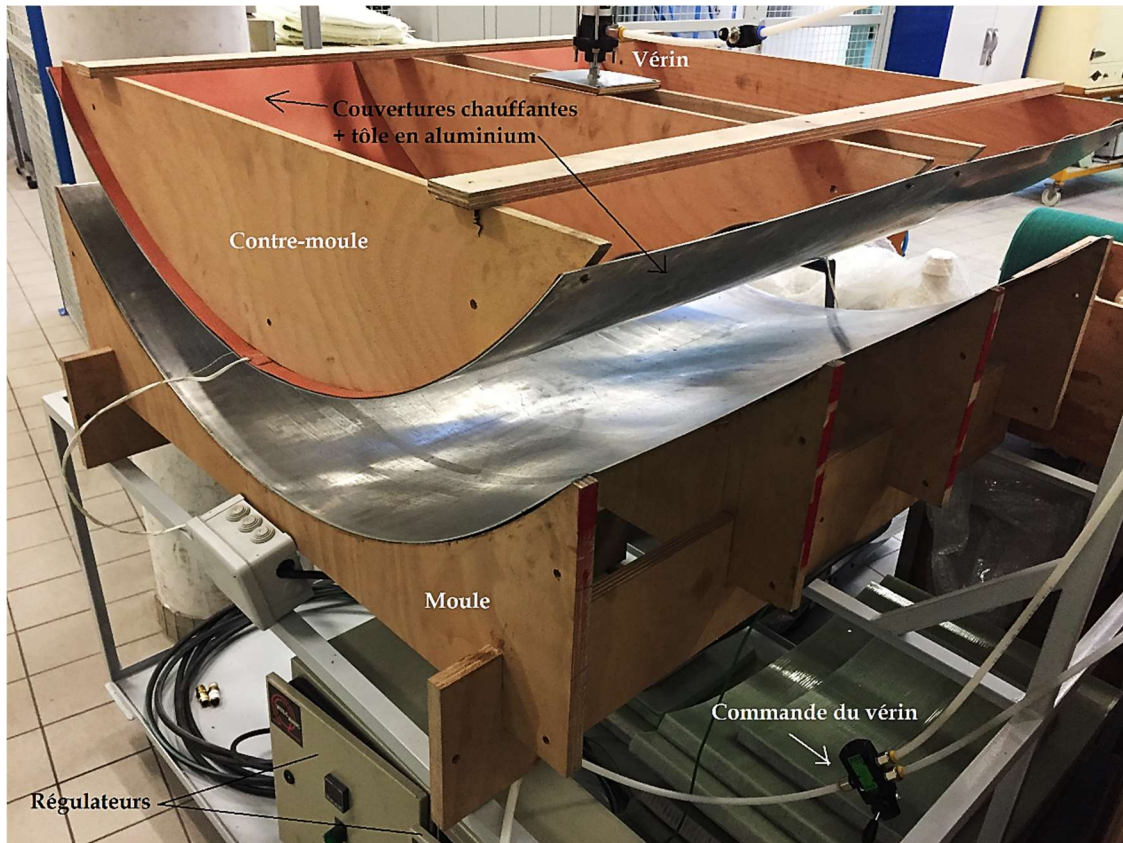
Equipement réel prototype de thermoformage des âmes en mousse PET.
